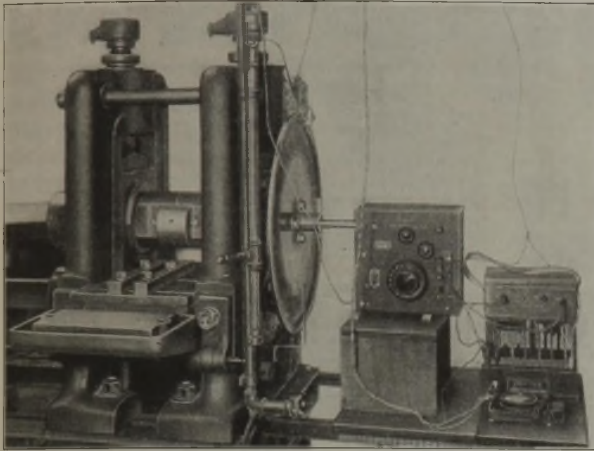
Walzwerk mit eingebauter Meßvorrichtung.
